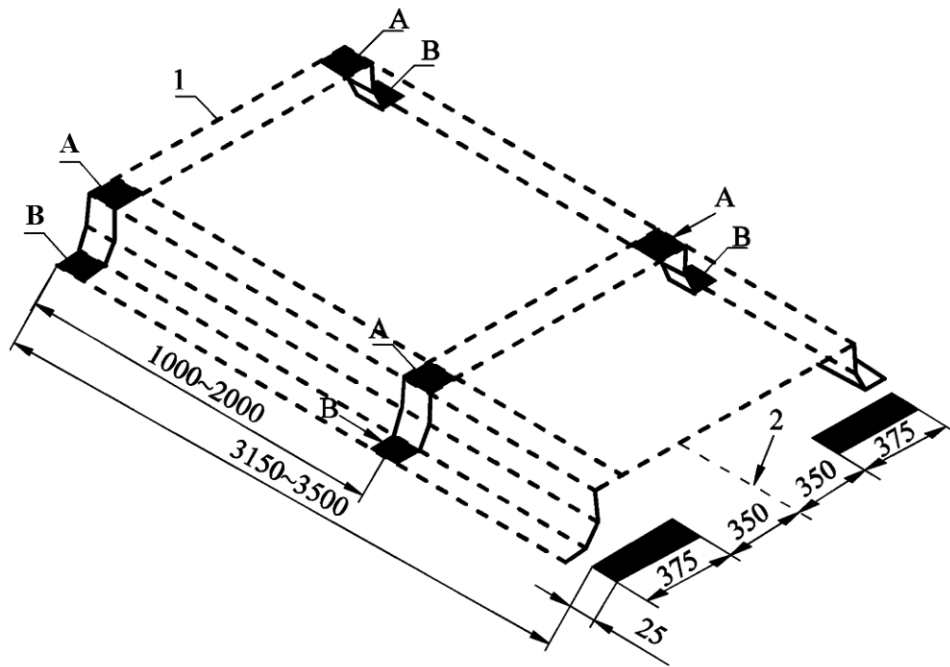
(1) 鹅颈槽断面图 (单位: mm)
